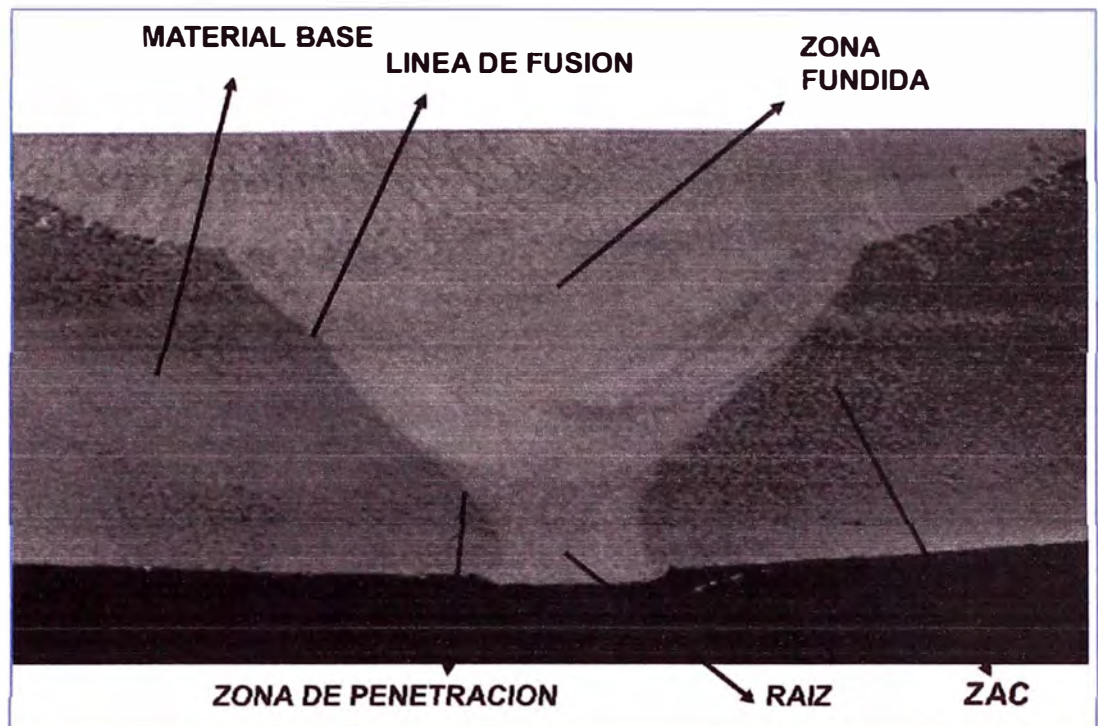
partes de una unión soldada. Se puede destacar la zona ZAC.
